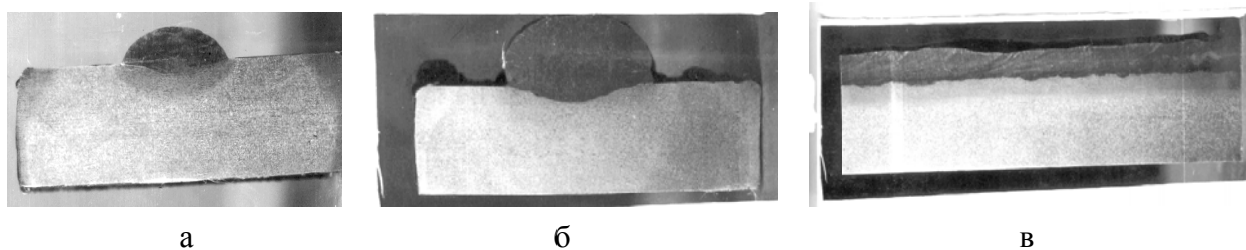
Вид макрошлифов однослойной и многослойной наплавки:
